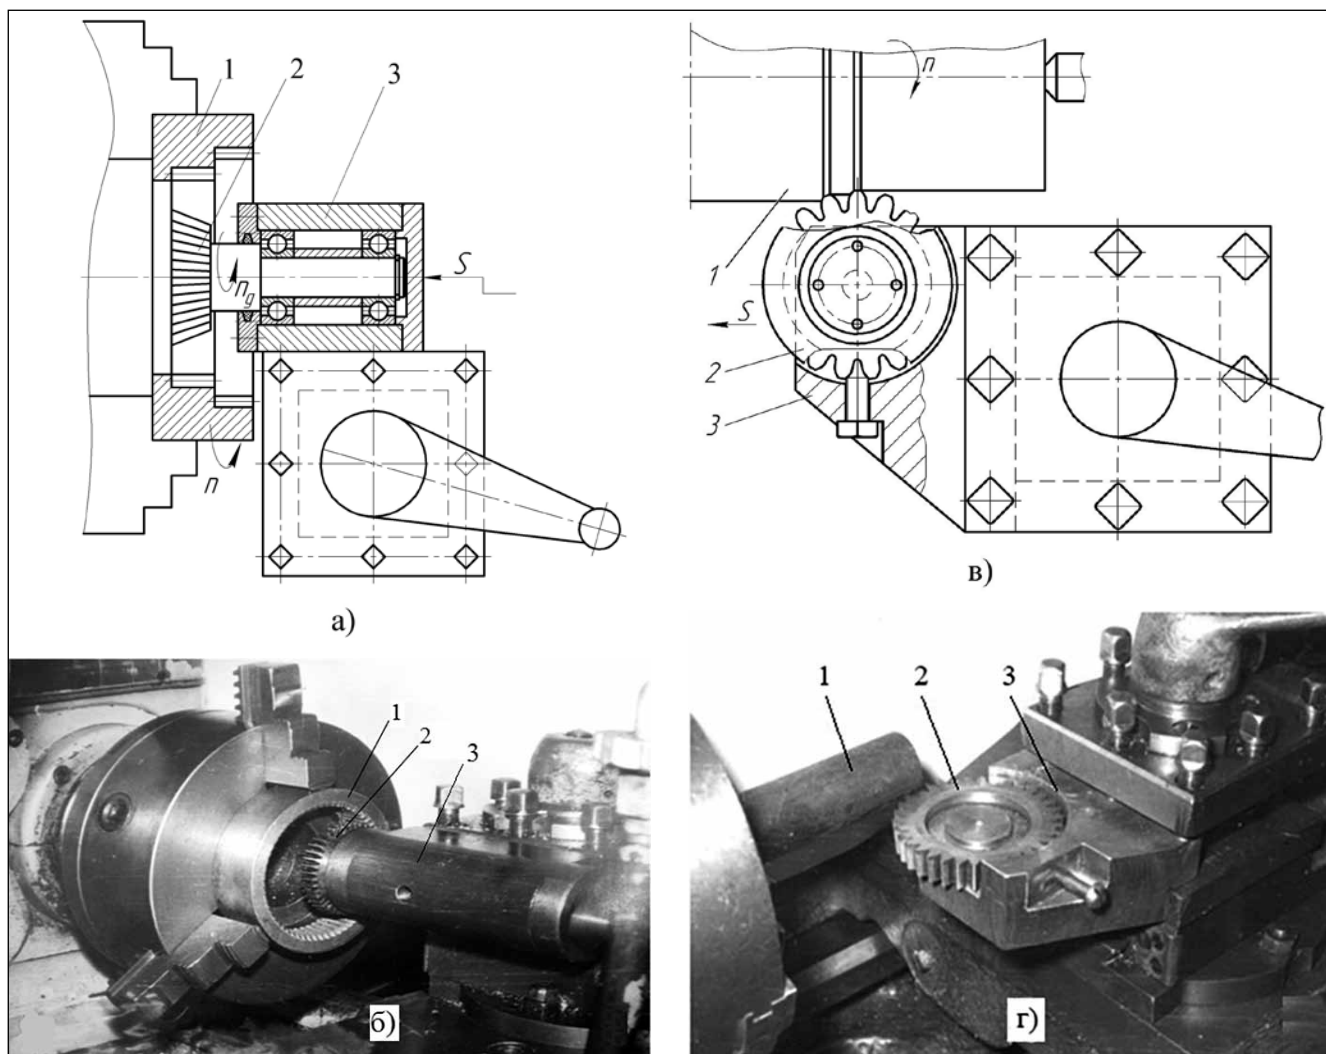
Зуботочение внутренних зубьев двувенцового колеса: а) схема, б) рабочая зона токарного станка. 1 — нарезаемое колесо, 2 — долбяк, 3 — приспособление; n и n_d — частоты вращения детали и долбяка, s — подача долбяка; в) схема точения долбяком, г) рабочая зона. 1 — заготовка вала, 2 — долбяк со сломанным зубом, 3 — приспособление к резцедержателю
